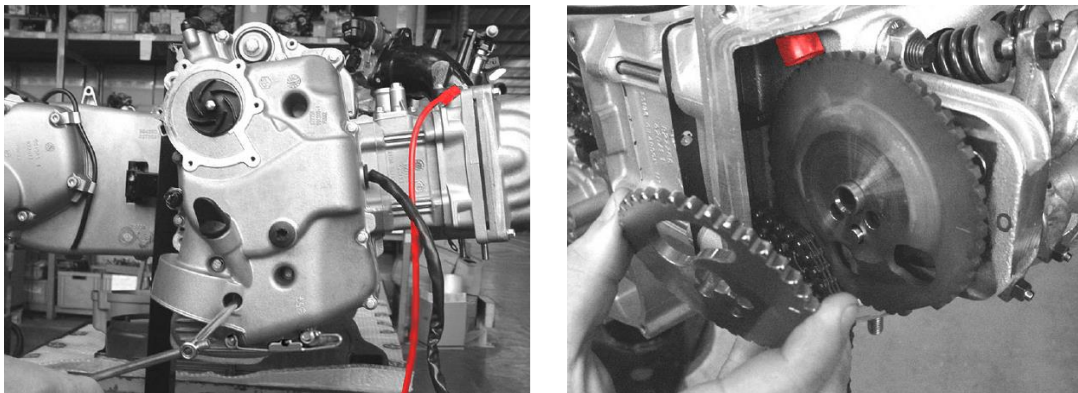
Censor de efecto hall del motor Piaggio 500cc
